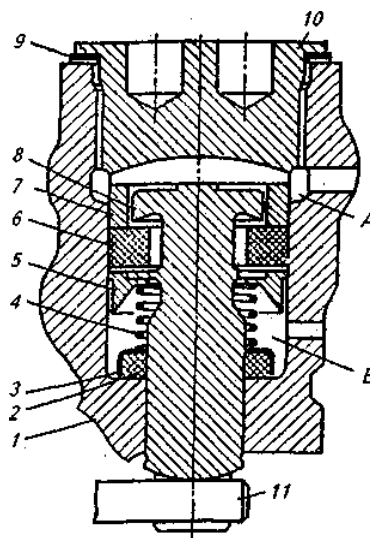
Регулятор давления автомобиля ВАЗ-2121: А, Б- полости регулятора; 1 — корпус; 2 — уплотнительное кольцо; 3 — обойма; 4 — пружина; 5 — тарелка; 6 — резиновый уплотнитель; 7 — распорная втулка; 8 — поршень; 9 — прокладка; 10 — пробка; 11 — торсион привода регулятора
